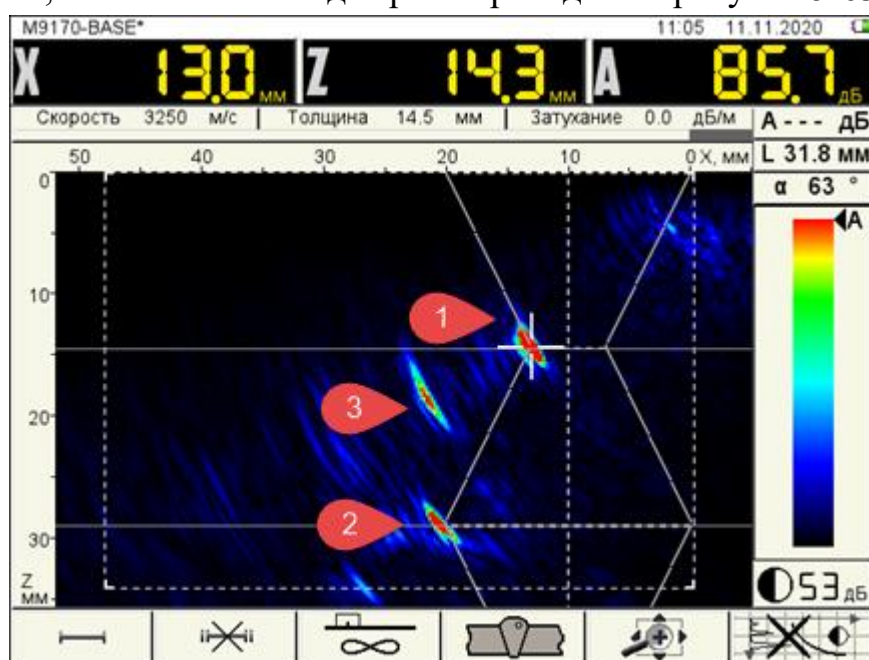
Образы ложных отражателей на сварном шве. Положение 1.
